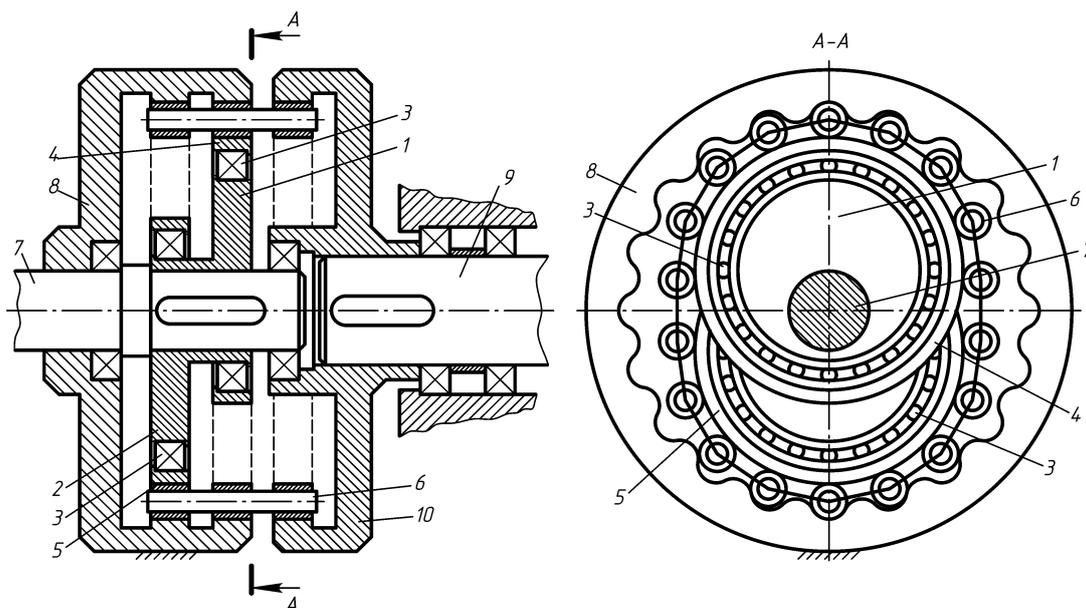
Конструктивная схема волновой передачи с трехрядной стандартной втулочно-роликовой цепью: 1, 2 – диски генератора волн; 3 – подшипники генератора волн; 4, 5 – кольца генератора волн; 6 – цепь; 7 – входной вал; 8 – неподвижное зубчатое колесо (корпус); 9 – выходной вал; 10 – ведомое зубчатое колесо
